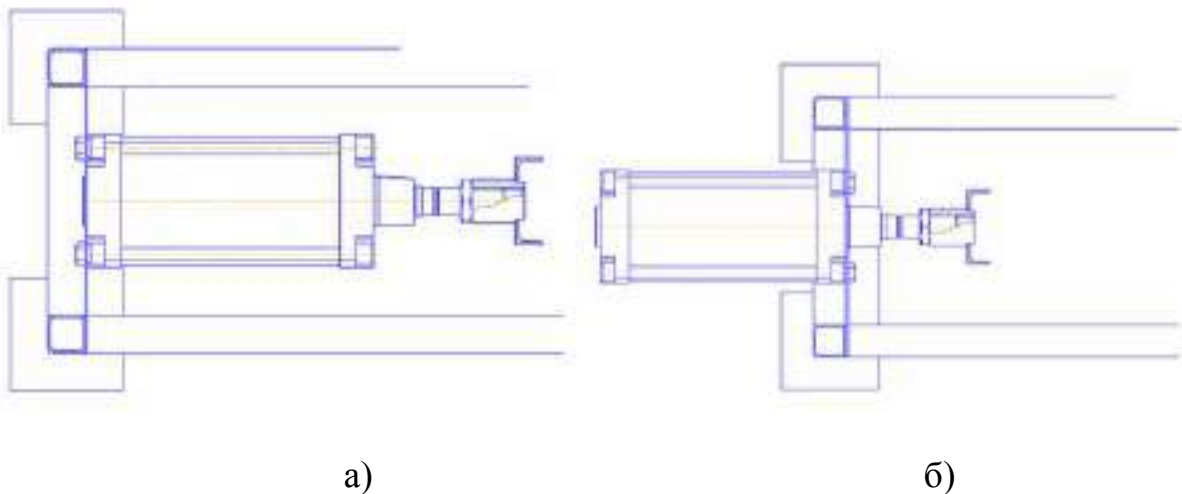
Варіанти кріплення циліндра до рами стенда.
